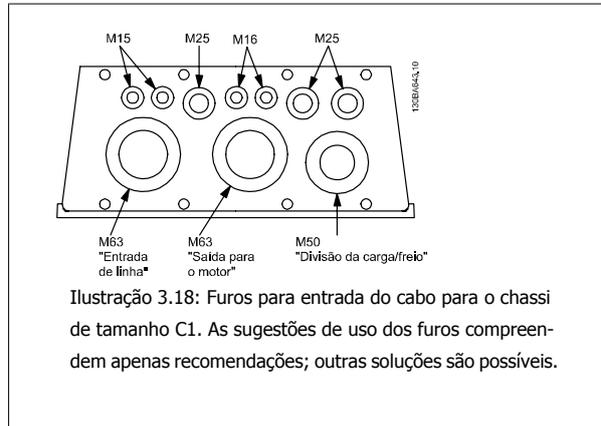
Furos para entrada do cabo para o chassis de tamanho C1. As sugestões de uso dos furos compreendem apenas recomendações; outras soluções são possíveis.
